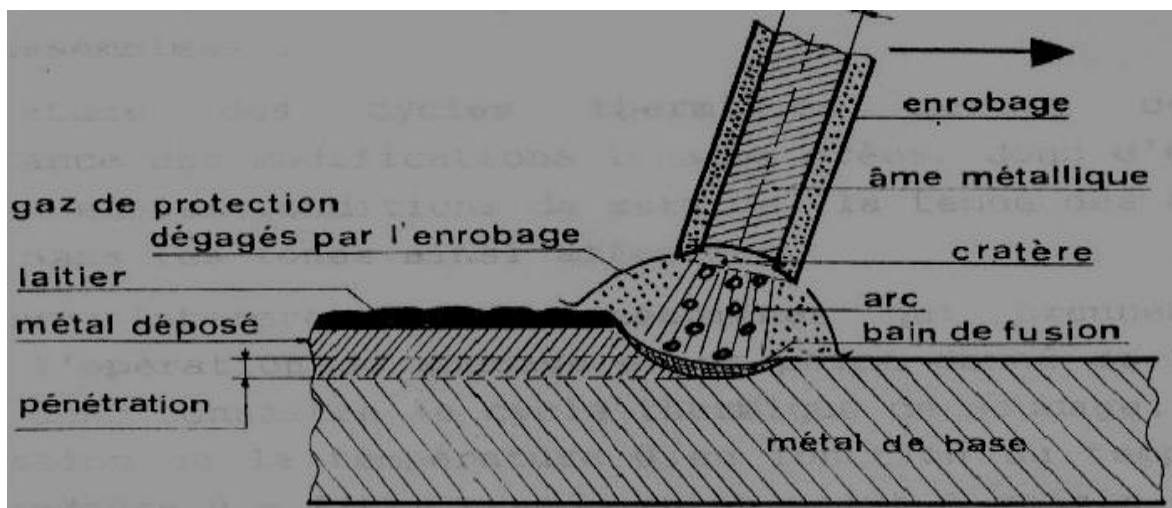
Soudage à l'arc électrique.[10]
